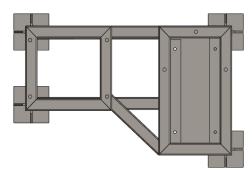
Vista isométrica inferior de estructura en perfil cuadrado.
